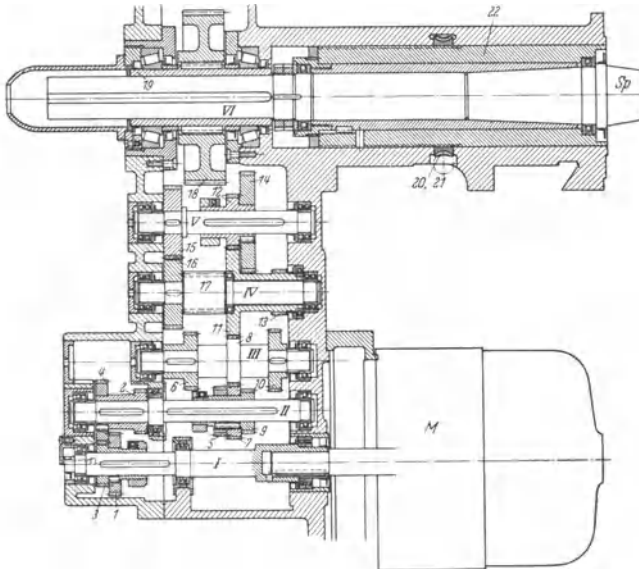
Frasspindelstock zur Langfräsmaschine Fig. 26 (Fa. Gildemeister).
